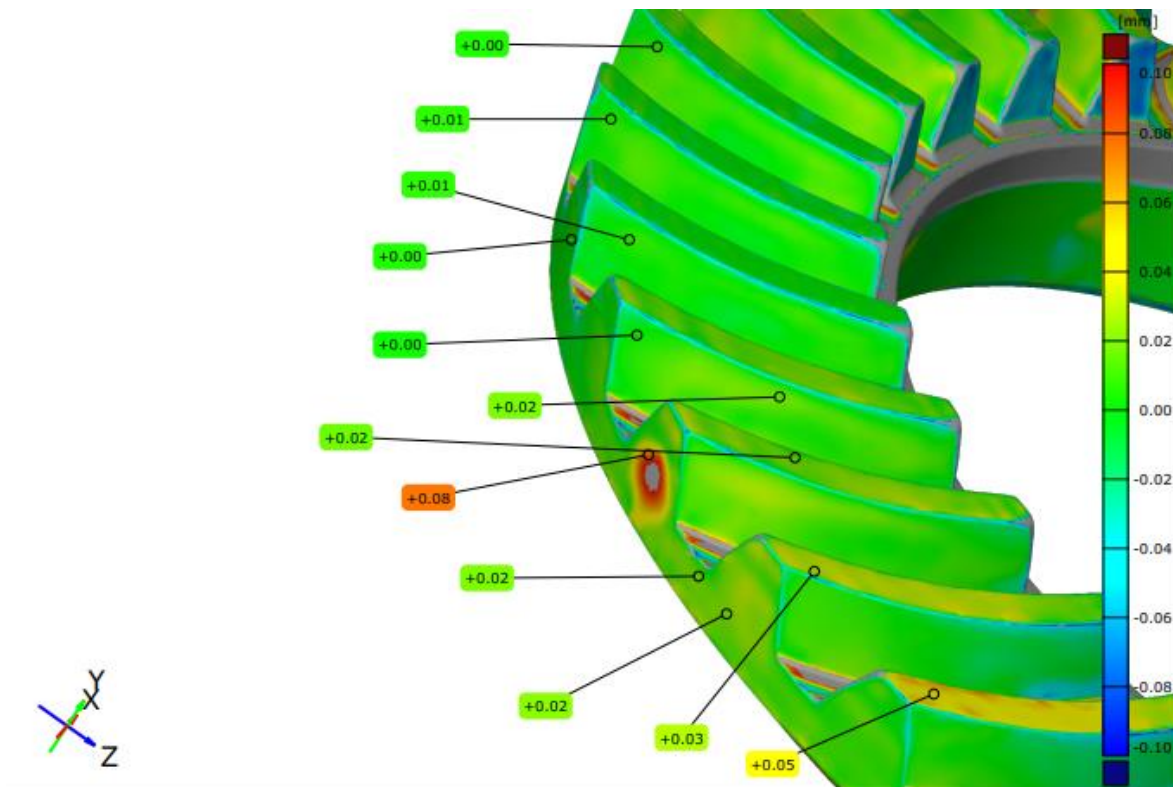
Rozměrová analýza zubů – kolo (detail).
